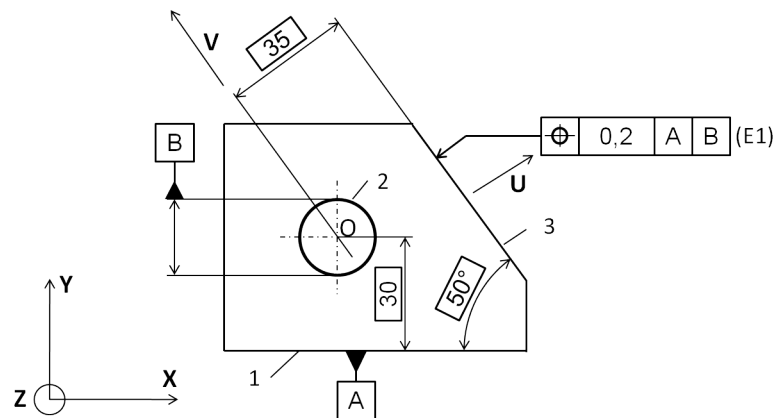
Localisation d'une surface plane par rapport à un système plan - cylindre
